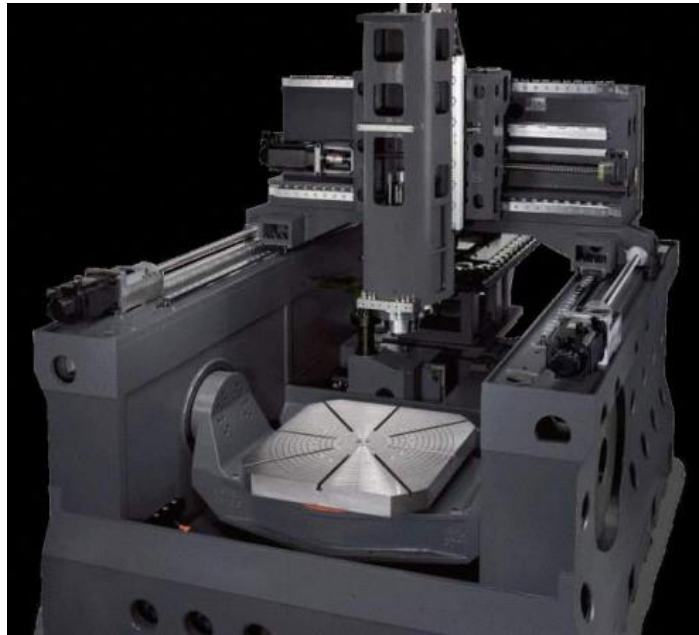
Фрезерно-гравірувальний верстат
